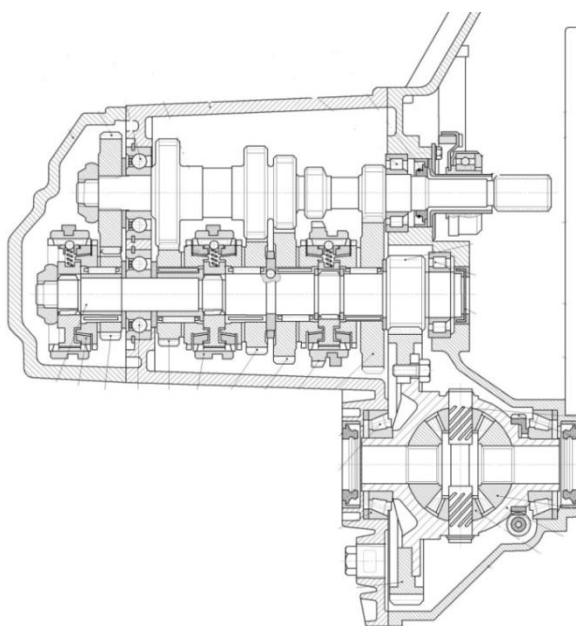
Конструкция пятиступенчатой КПП ВАЗ-2108
